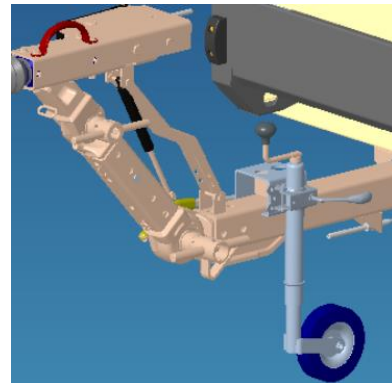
Opěrné kolečko KNOTT TK60 [27]
